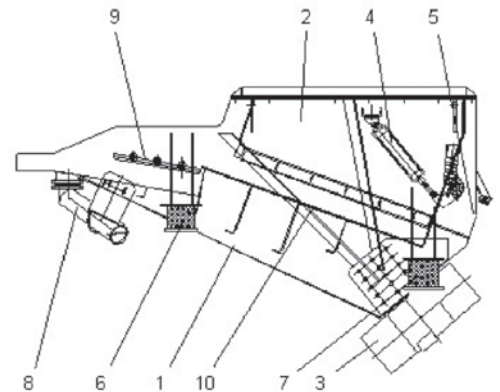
Конструкция дробилки: 1 – корпус; 2 – камера дробилки; 3 – дебалансированный электродвигатель; 4 – пневмоцилиндр; 5 – отверстие для удаления грубых частиц; 6 – передняя резинопневматическая рессора; 7 – задняя резинопневматическая рессора; 8 – отводная труба для песка крупных фракций; 9 – зона просева; 10 – износозащитная листовая обшивка
